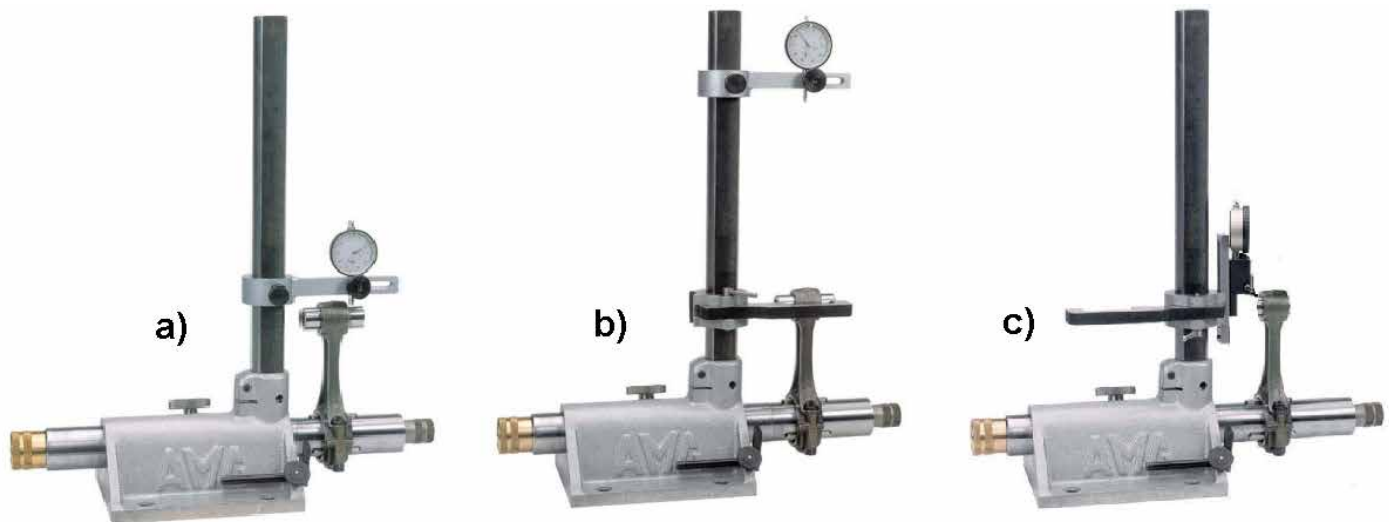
HW23*: Приспособление для проверки шатунов. а) проверка изгиба шатуна; б) проверка шатуна на скручивание; в) проверка верхней головки шатуна на смещение; источник: *AMC-SCHOU A/C*.
